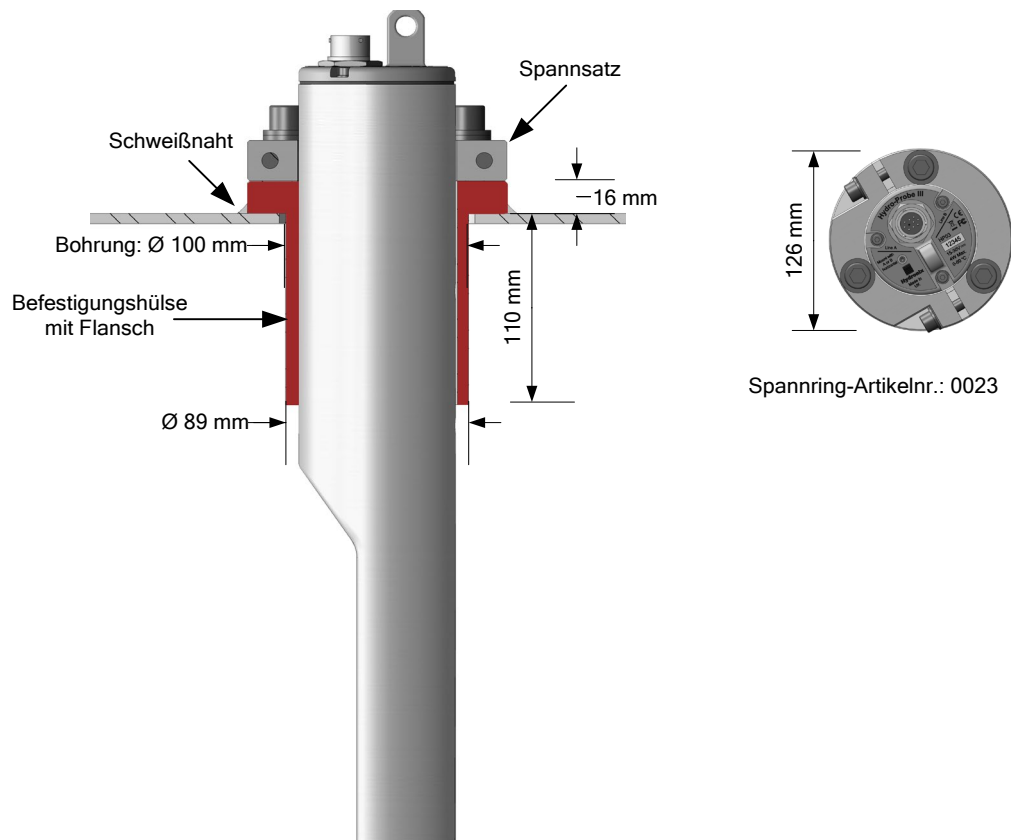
Befestigungshülse mit Flansch (Artikelnr. 0024A)
